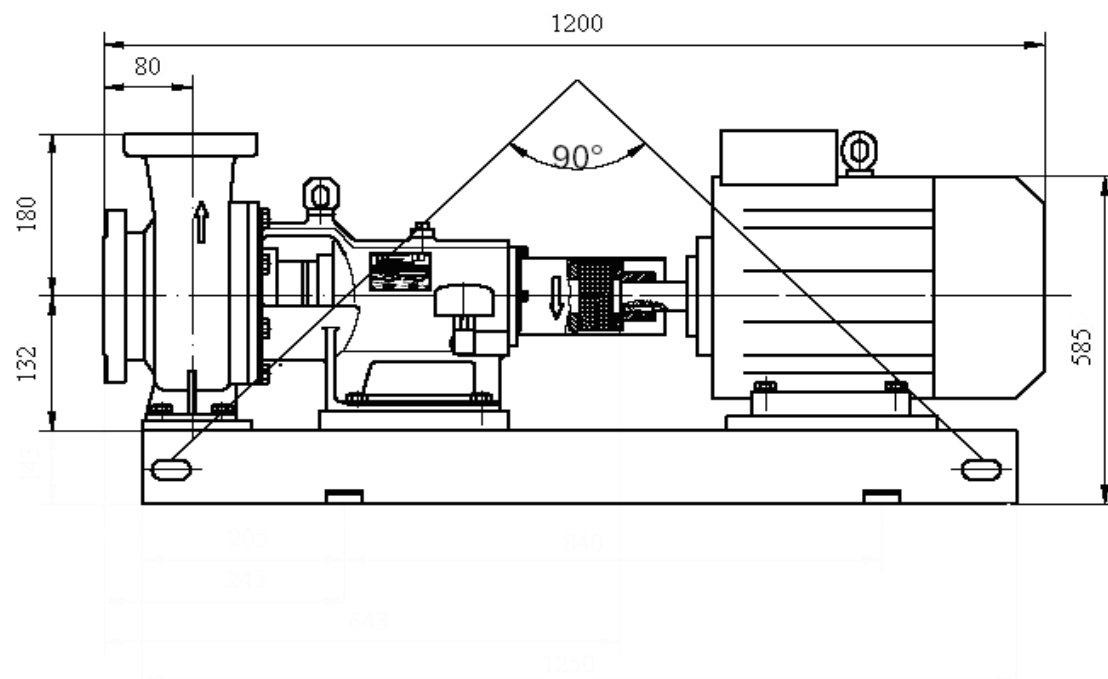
Габаритный чертеж насоса GMH10AP001
